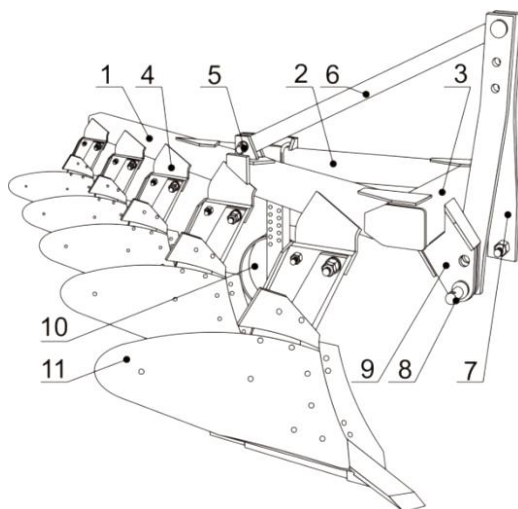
Общий вид плуга рыхлителя ПРУН-5-45
